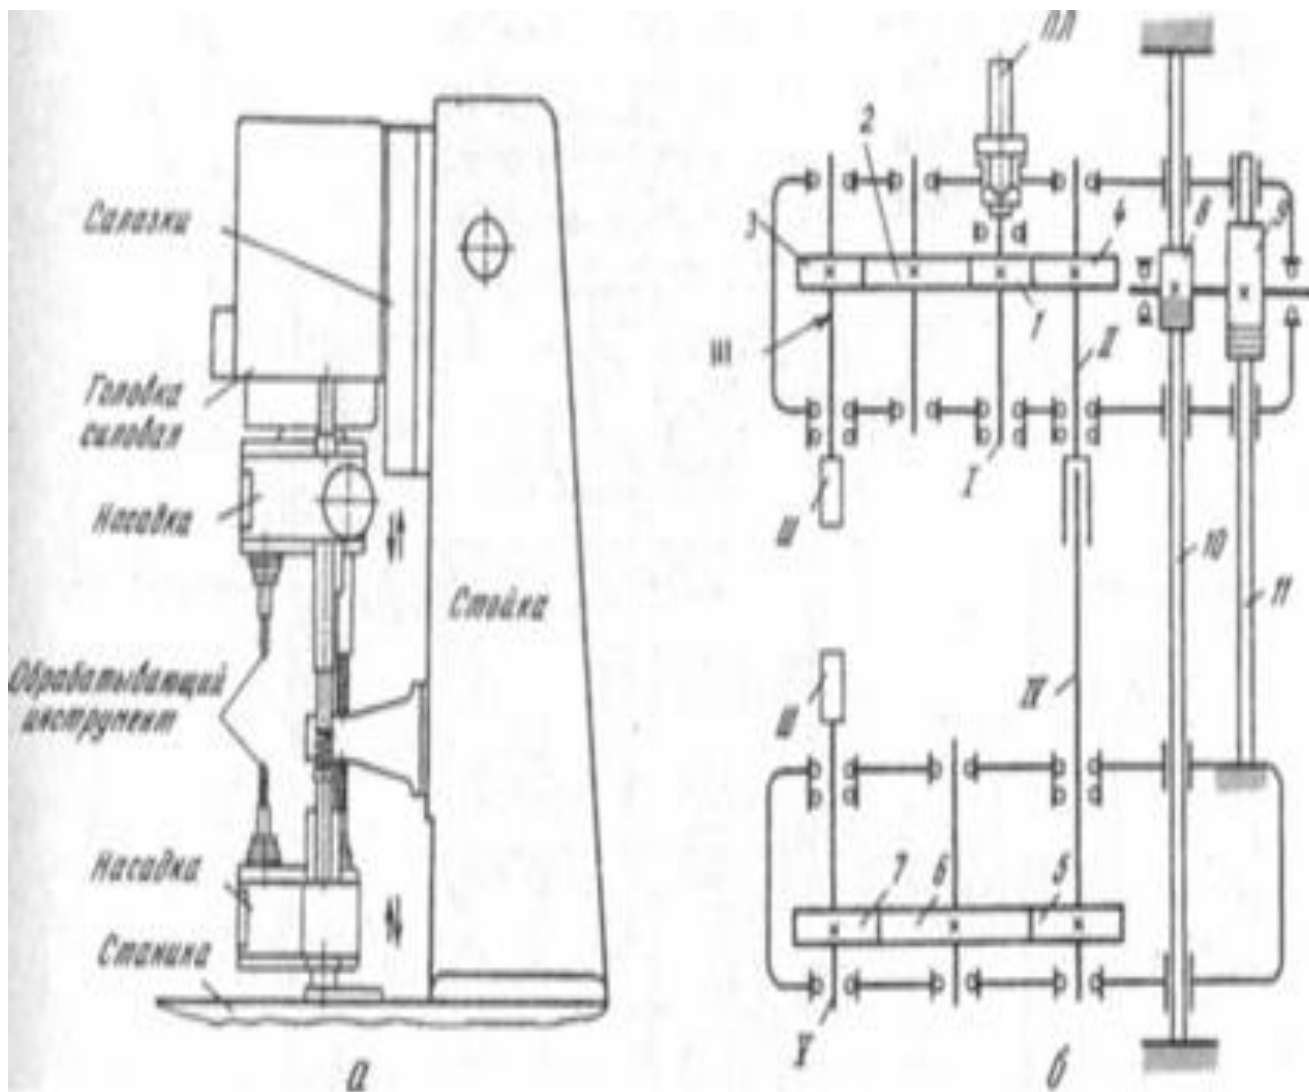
Механизм для двухсторонней обработки: а – общий вид, б – кинематическая схема.
